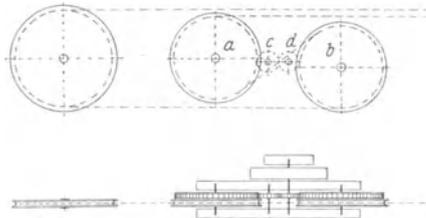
Seilantrieb mit zwei einrilligen Antriebscheiben.
